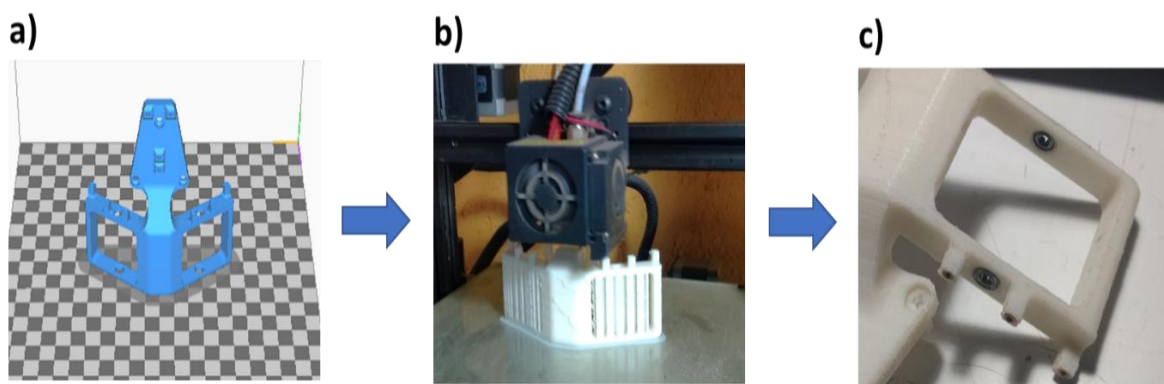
Proceso de manufactura de los elementos mecánicos del arreglo instrumental, a) diseño de la pieza, b) manufactura de la pieza, c) acabado final e incorporación de elementos mecánicos.
